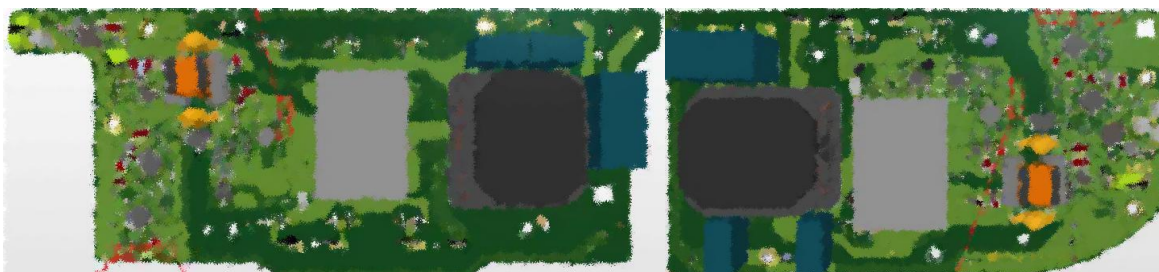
PCBA 8KW/PCBA 5.2KW da MOPF. (Borgwarner)
